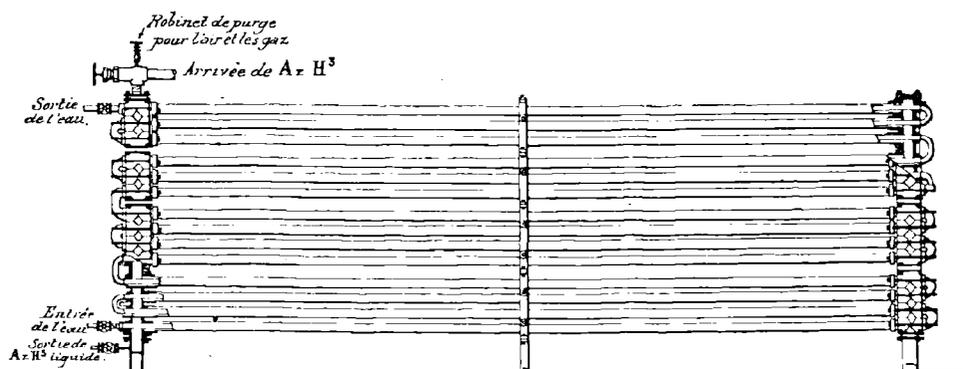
Condenseur à double tuyau (type Buffalo Refrigerating Machine C°).
